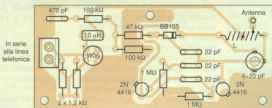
Montaggio dei componenti sul circuito stampato del trasmettitore.
